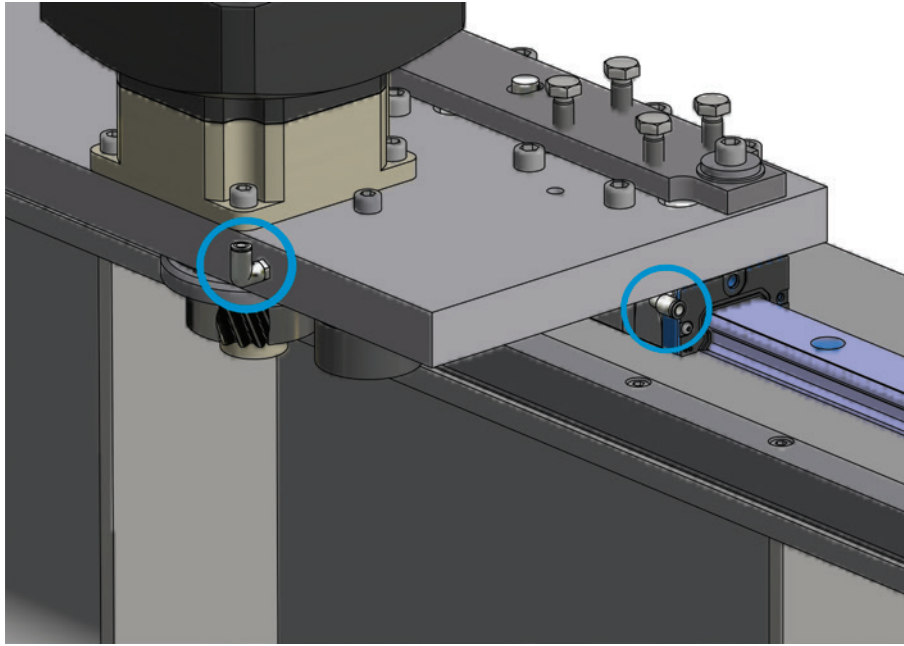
Schmieranschlüsse für Zentralschmiersysteme
